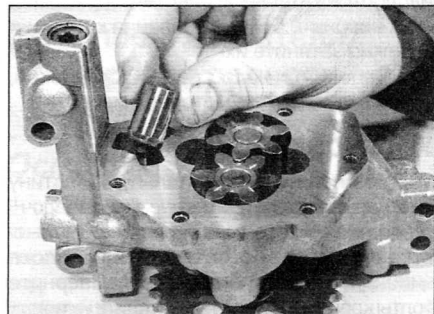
, в. ...и поршень предохранительного клапана, отметив для себя, как он установлен
